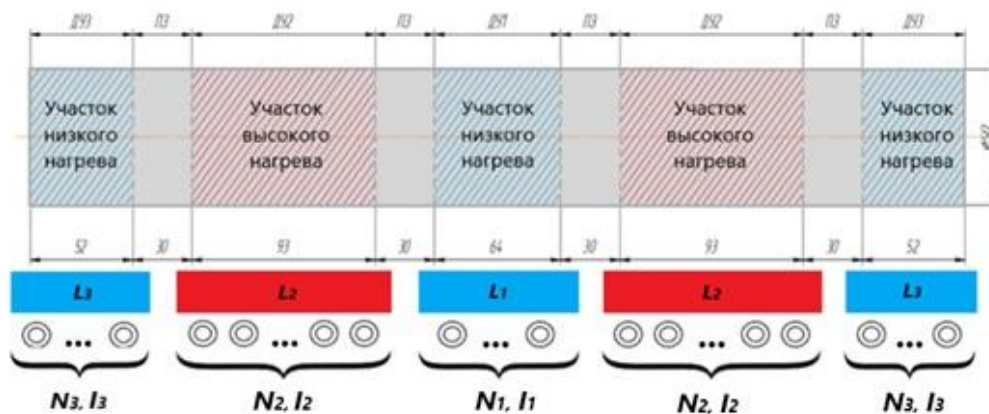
Схема расположения индуктора относительно стальной заготовки
